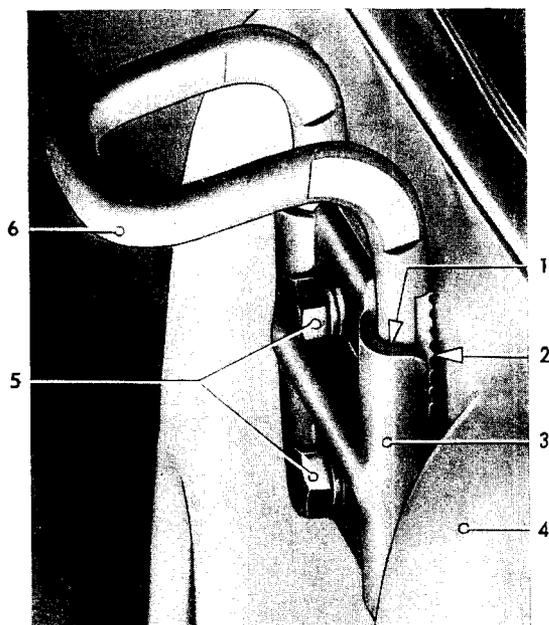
Schließbügel in Grundeinstellung angeschraubt
